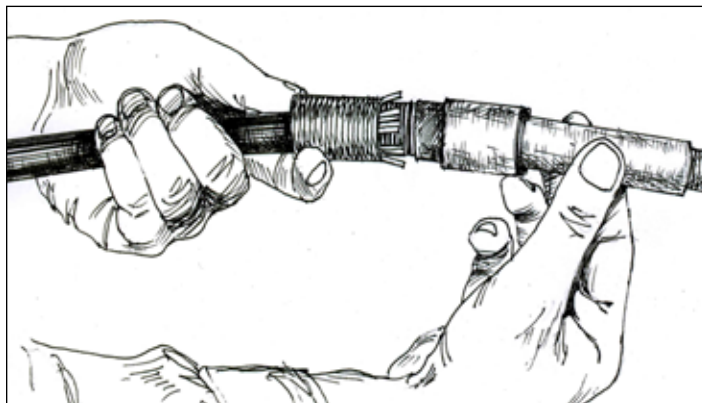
Установка внутренней гайки штуцера на проволоки брони
